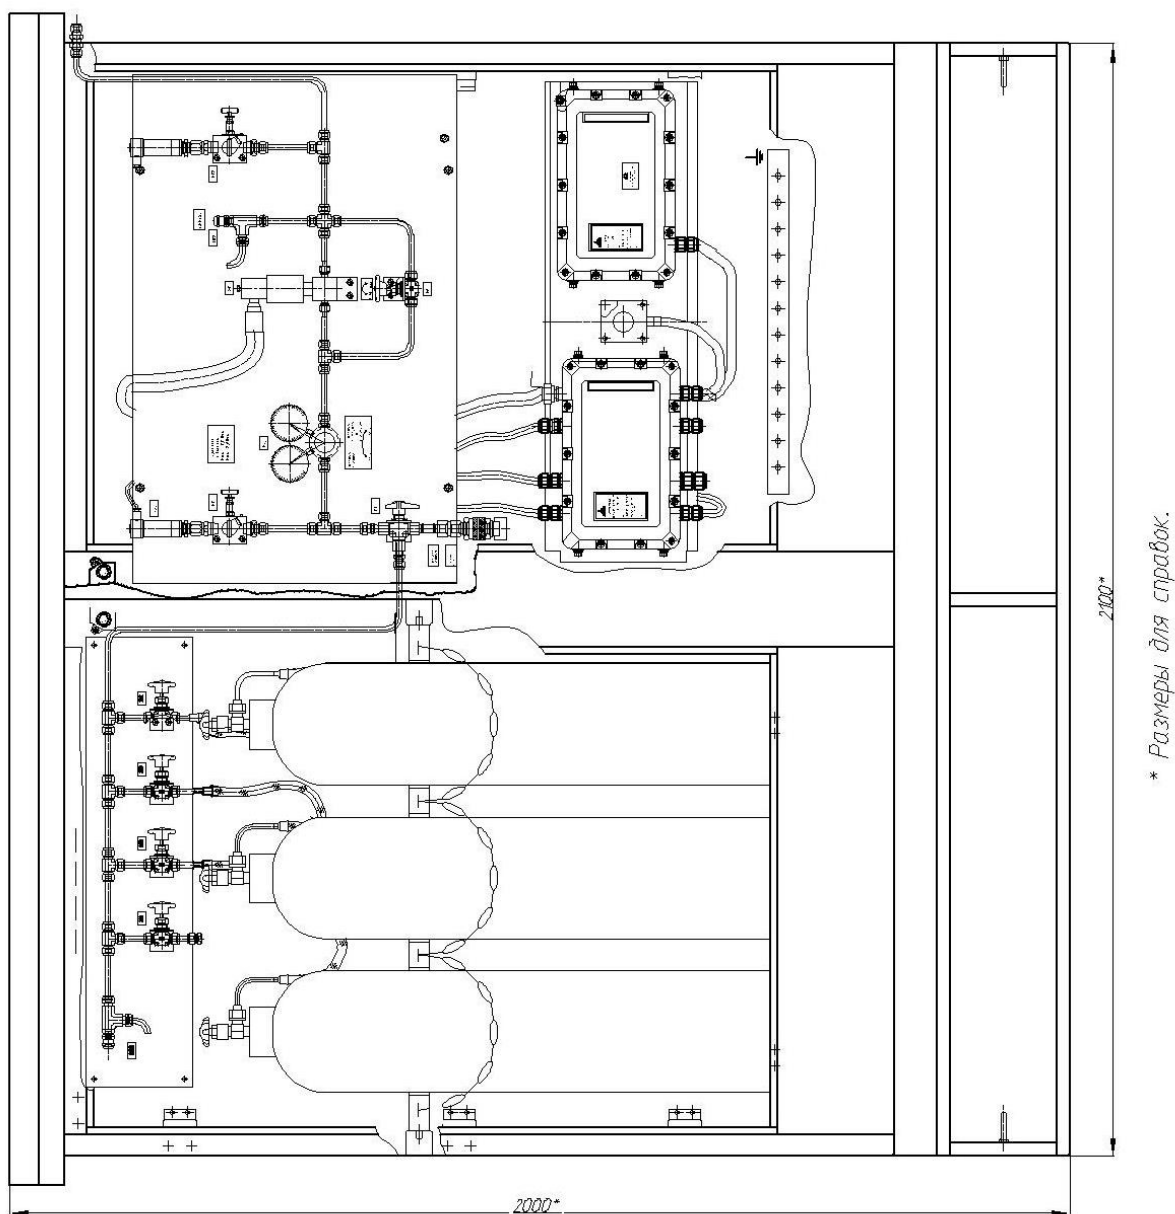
Внешний вид и габаритные размеры системы «АСДУК-П»
